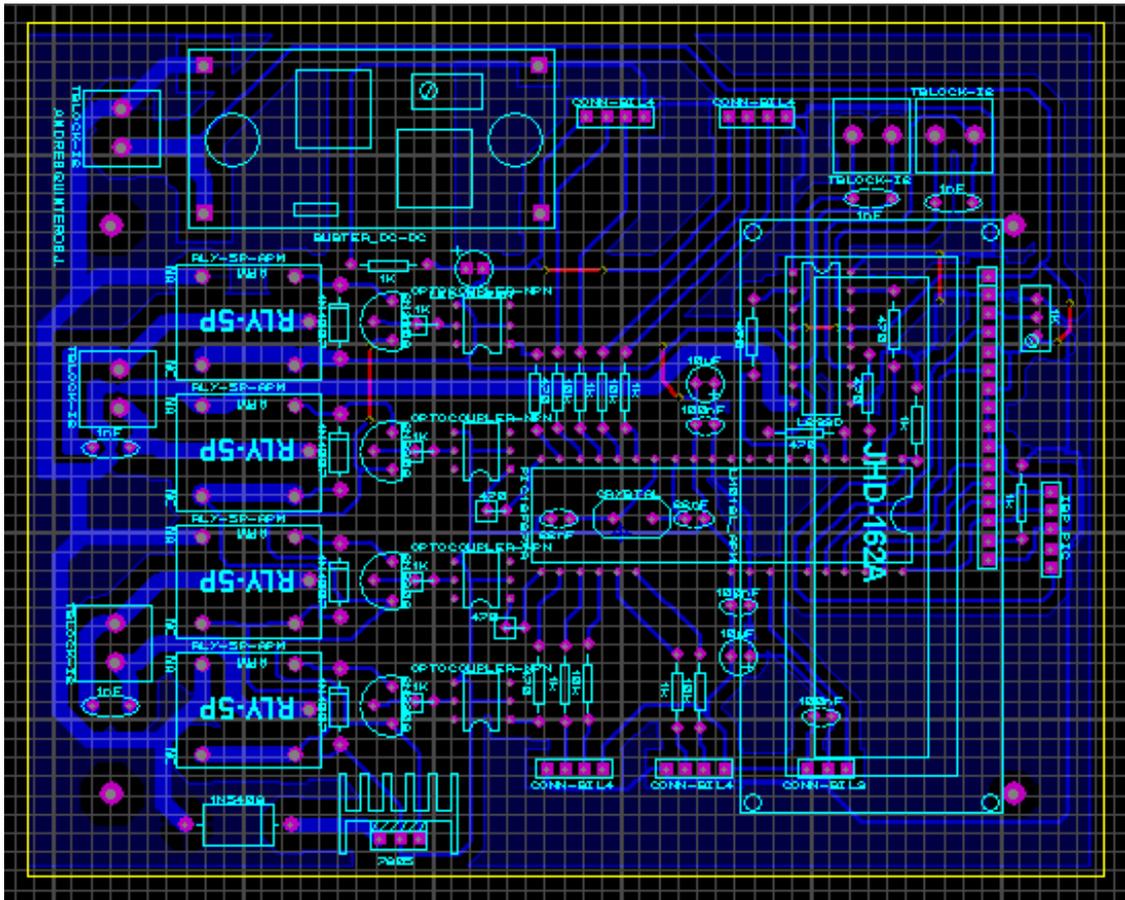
Diseño PCB del prototipo de robot recolector
